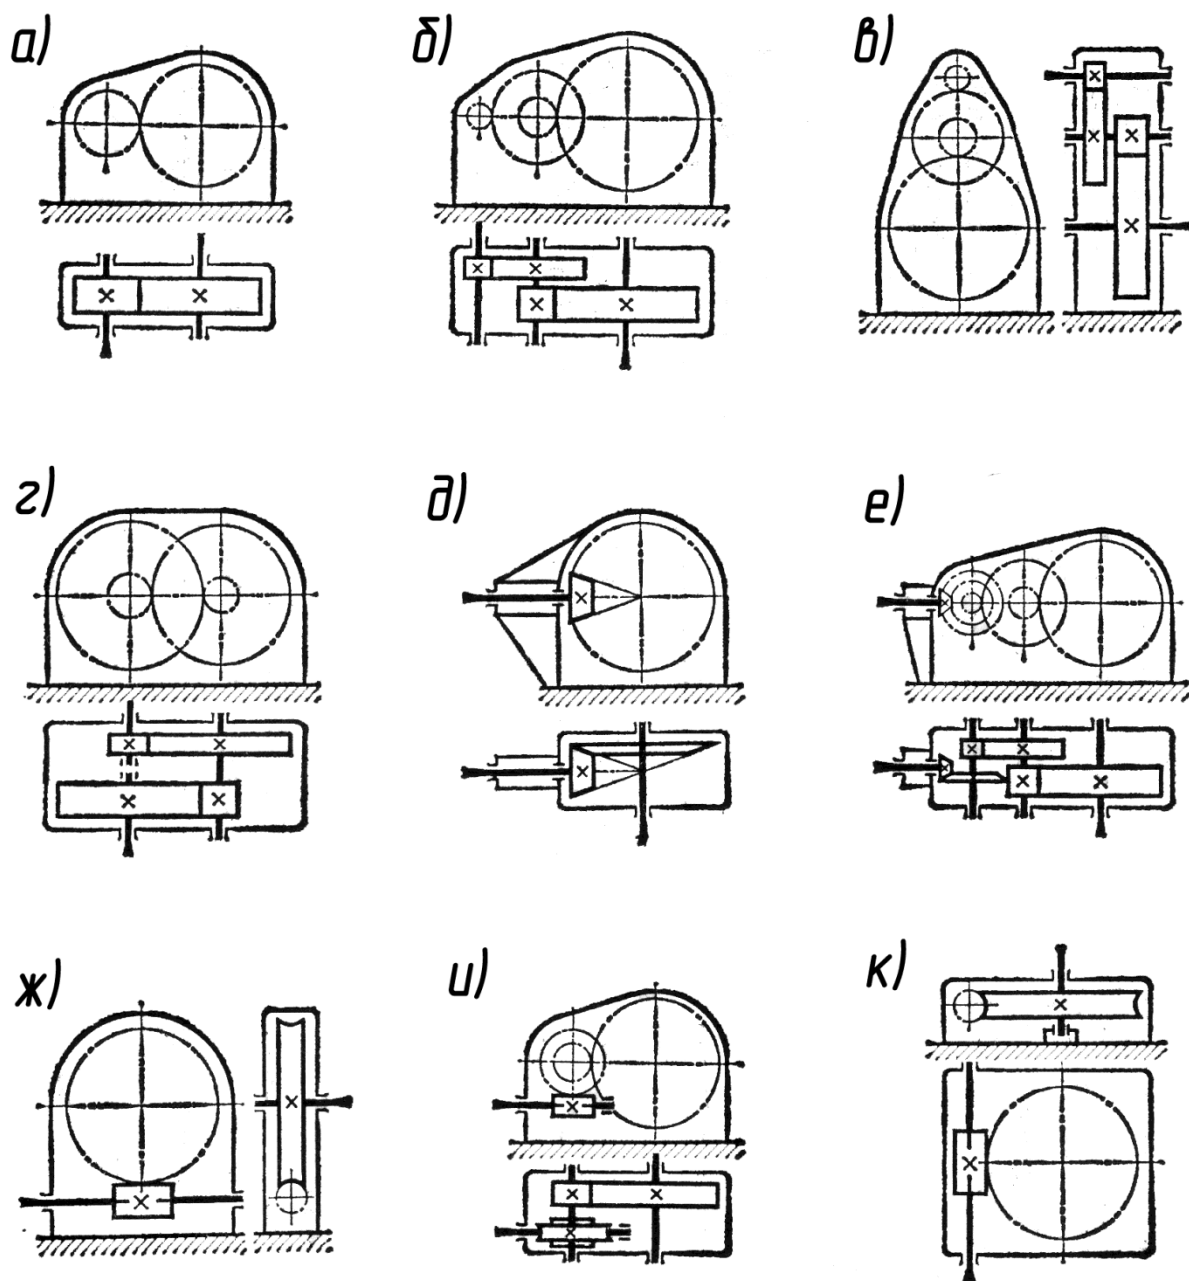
Кинематические схемы некоторых типов редукторов.
